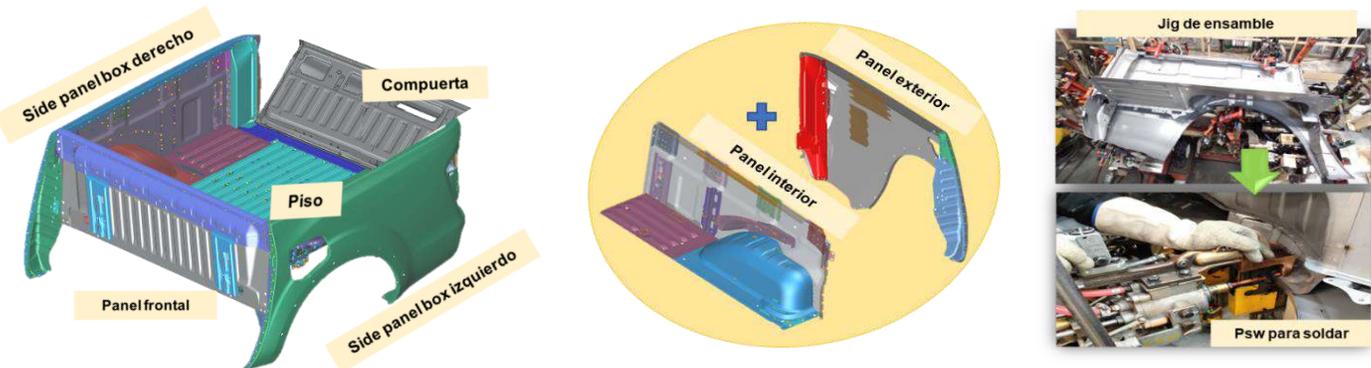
Componentes de la caja de carga y de los side panel box y dispositivos para soldar.
